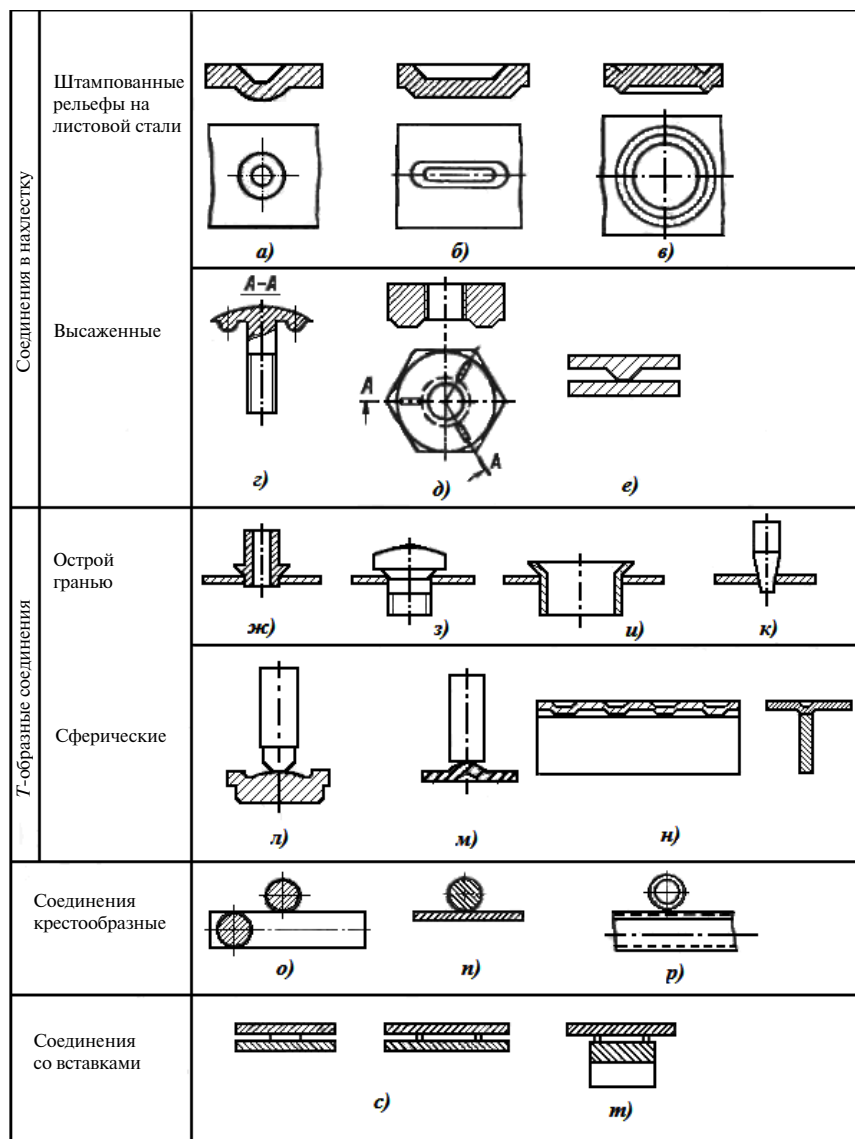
Конструкции соединений рельефной сварки
